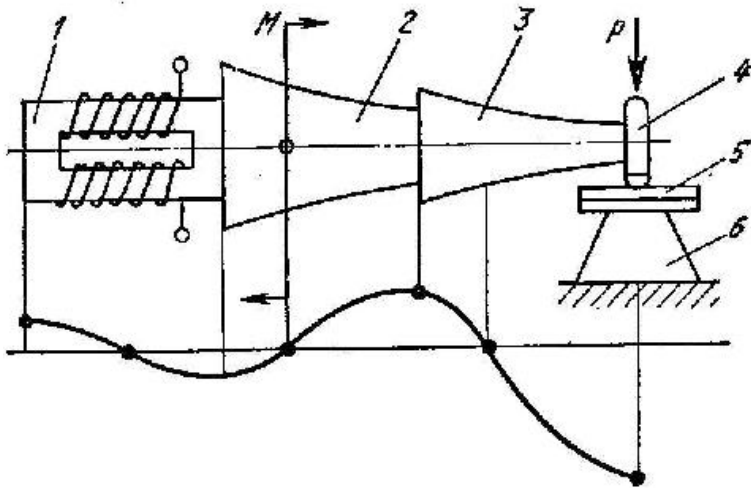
Принципиальная схема ультразвуковой сварки:
